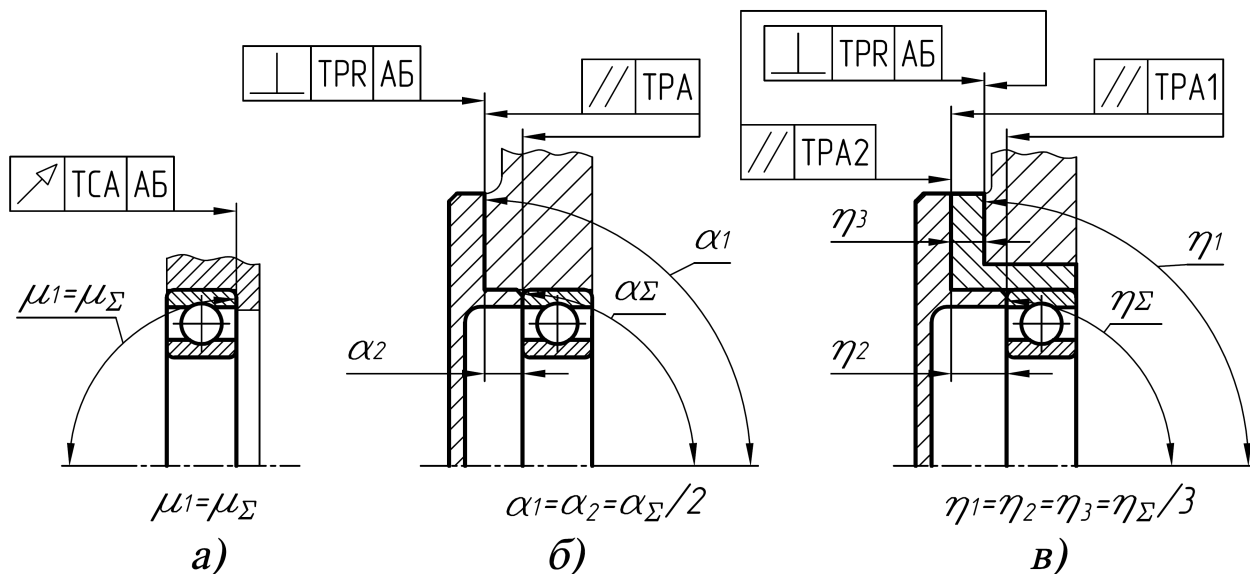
Схеми установки зовнішнього кільця підшипника кочення
